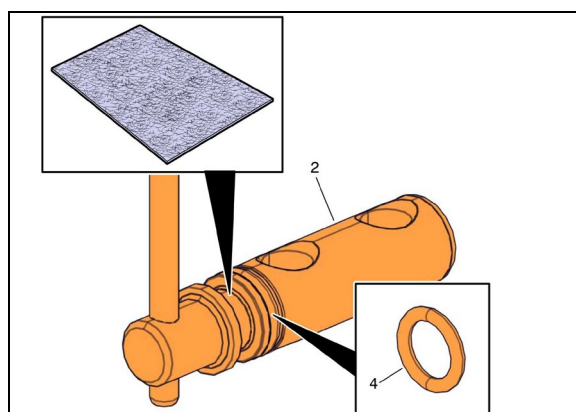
INSPECCION E O-RING (4) EN EL HUSILLO (2)
